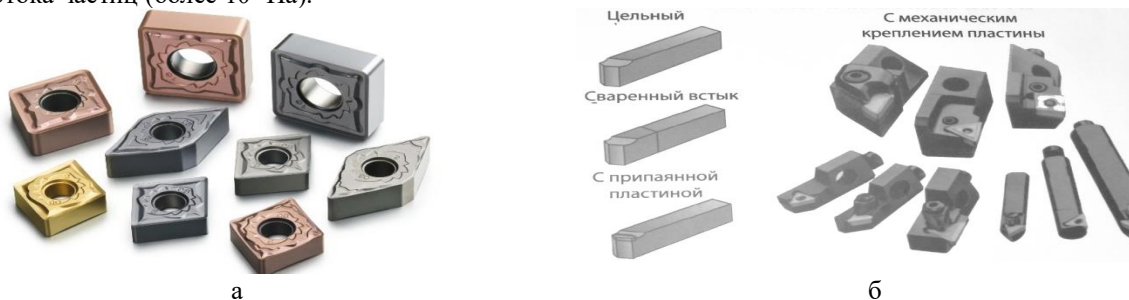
Твердосплавные пластины для резцов и способы их крепления
